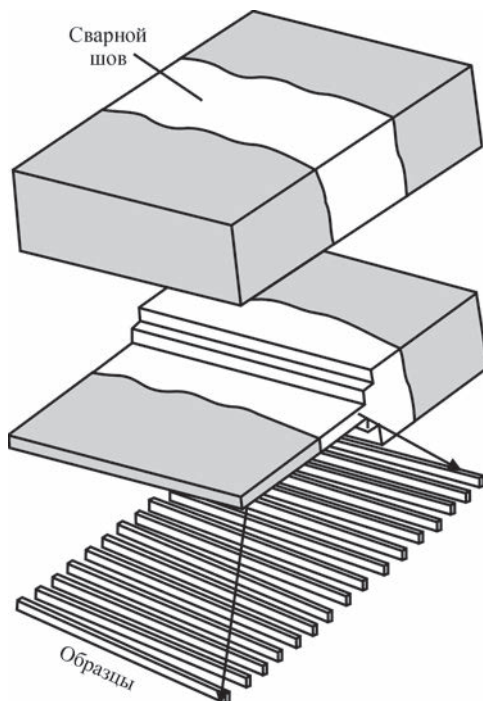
Схема изготовления образцов из сварного соединения
